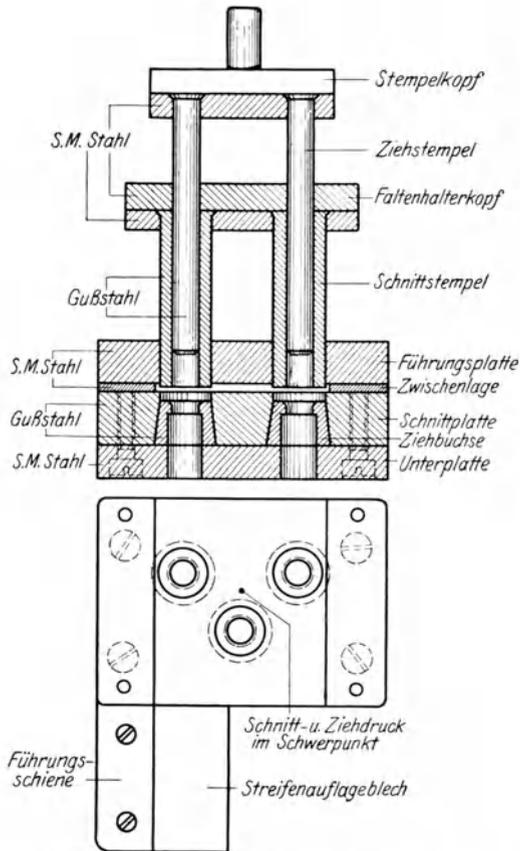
Dreifach wirkendes Schnitt- und Ziehwerkzeug für Schnitt- und Ziehpressen.
